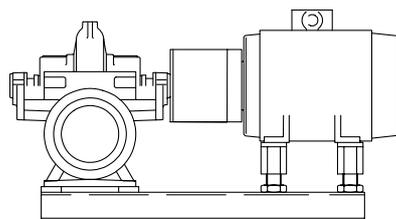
Тип установки ЗЕ - насос и двигатель на общей опорной раме
